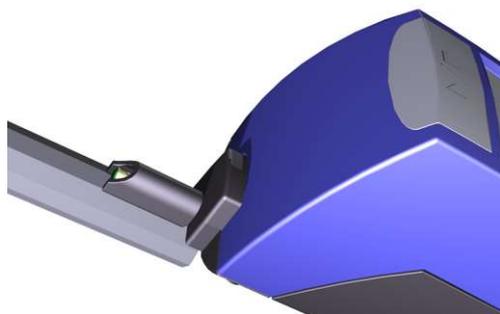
W5 mit Auflageprisma auf kleiner Welle
